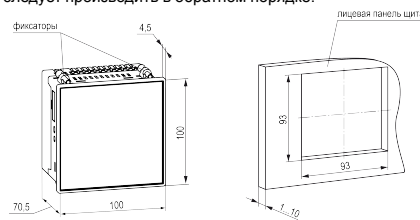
Габаритные размеры и монтажного отверстия в щите
